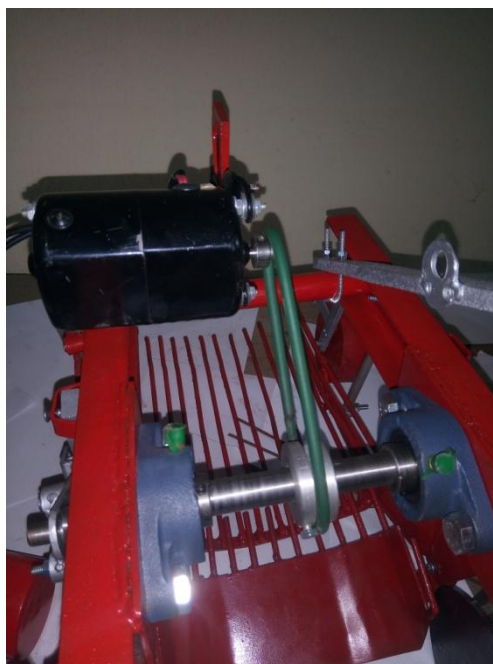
Moteur électrique et arbre récepteur du prototype
